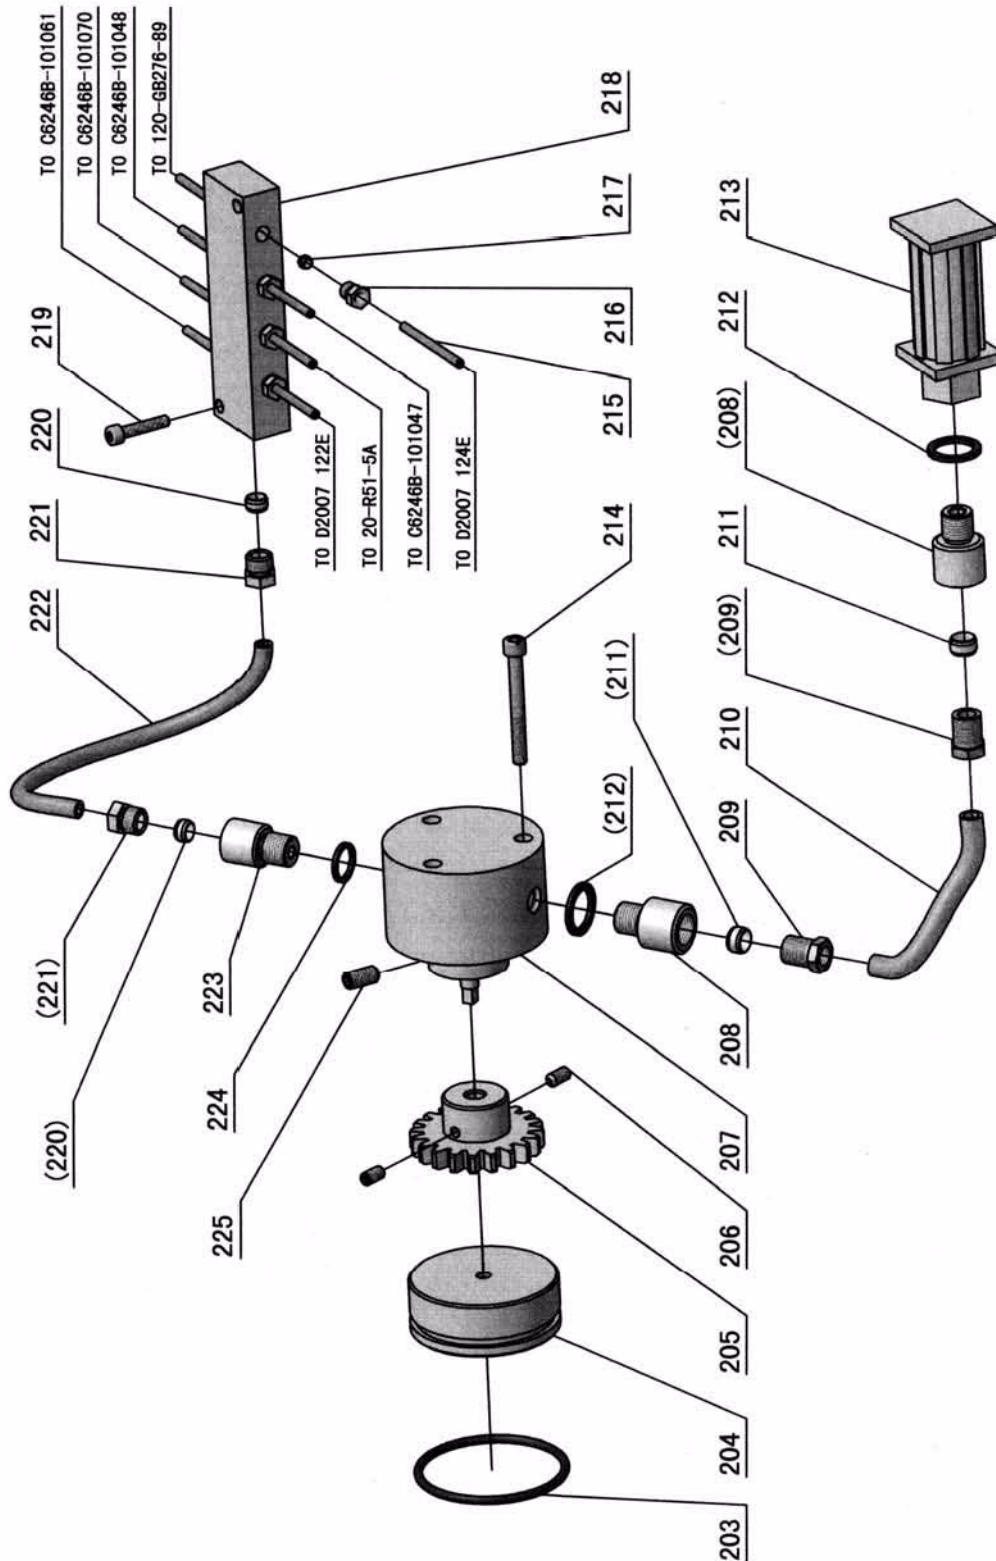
Spindelstock 8 von 8 - Headstock 8 of 8
